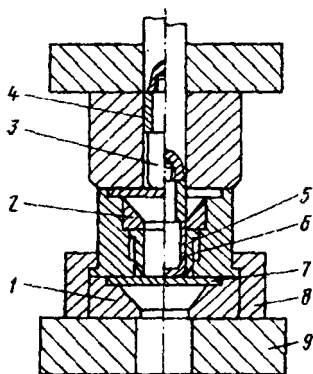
Схема штампа для послойной вытяжки двухслойных изделий
